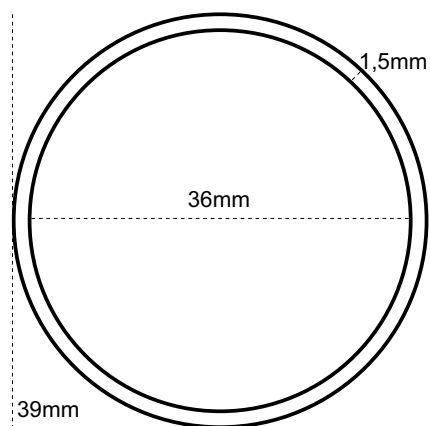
Schemazeichnung Leerzylinderphantom, Horizontalschnitt
